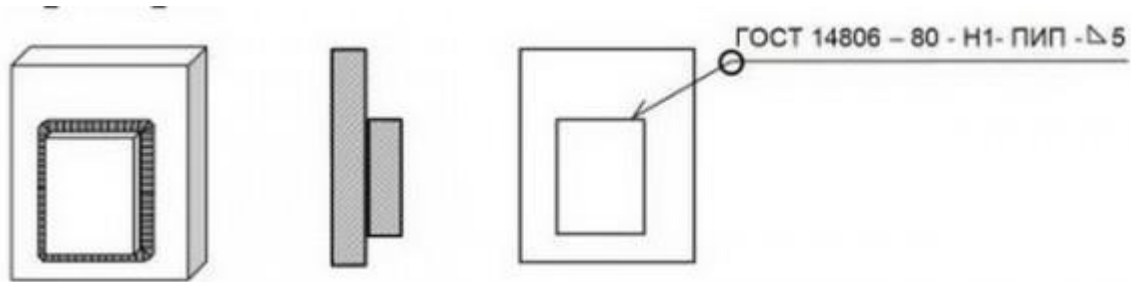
Дуговая полуавтоматическая сварка, чертеж
